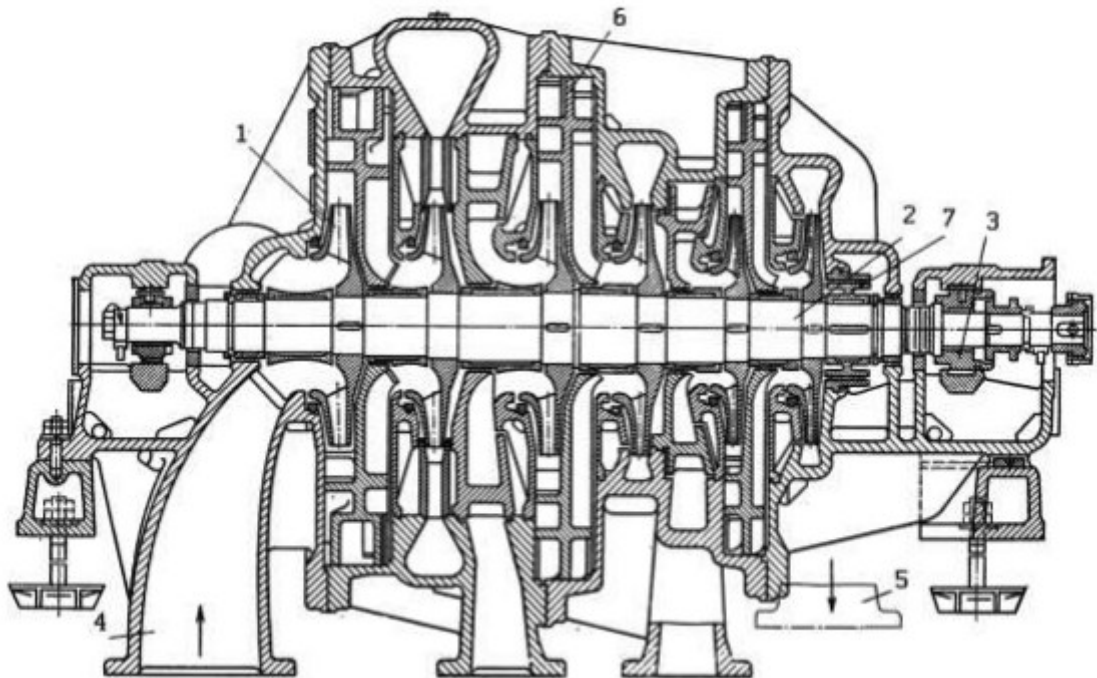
Повздовжній розріз компресора К-500-61-1: 1 – робочі колеса; 2 – вал ротора; 3 – підшипники; 4 і 5 – відповідно підвідний і напірний патрубки; 6 – діафрагма; 7 – думміс.
